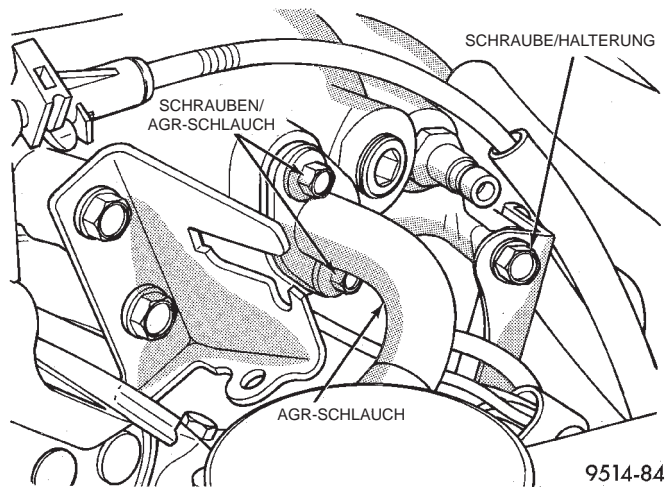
AGR-Schlauch und Schraube der rechten Halterung des Ansaugluftsammlers
